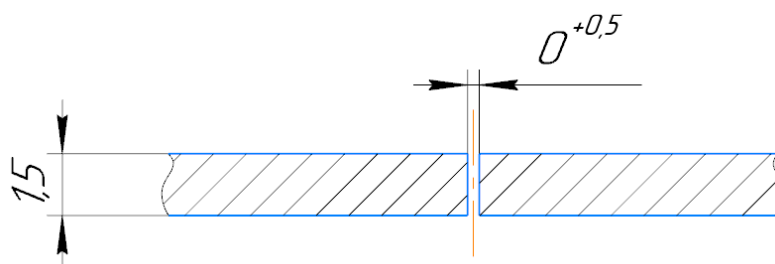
Геометрические параметры сборки пластин под сварку
